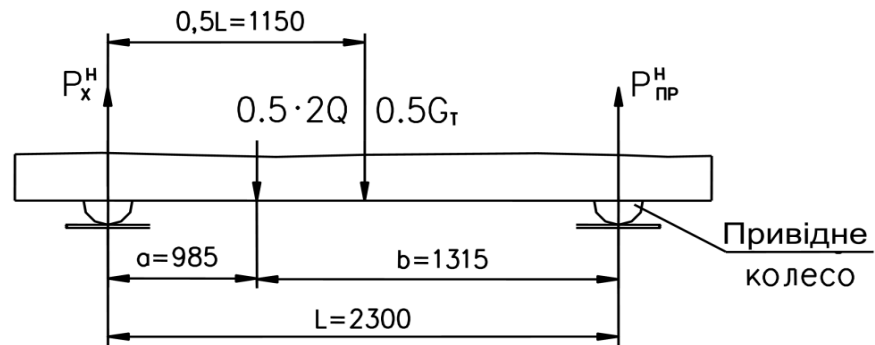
Схема навантажень на кінцеву балку візка при підйомі номінального вантажу.
